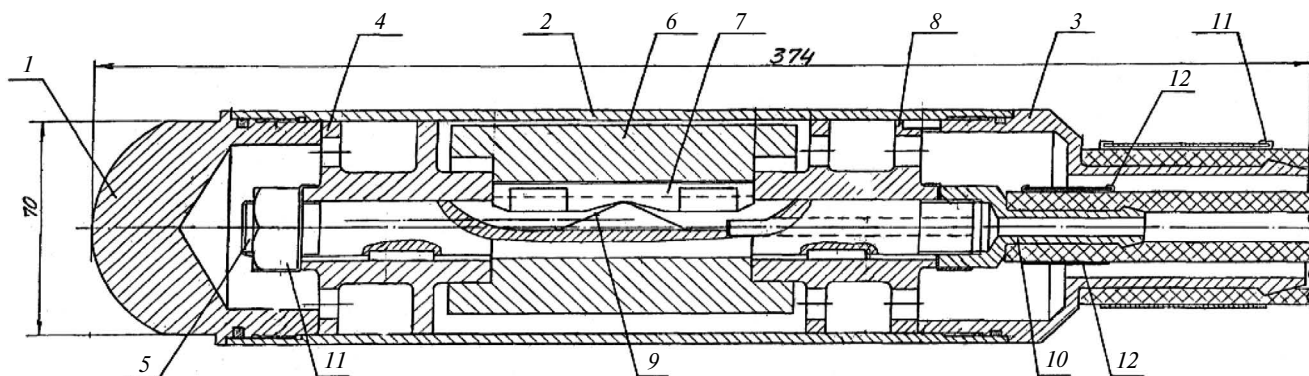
Глубинный пневматический вибратор: 1, 3 – оголовки; 2 – цилиндр; 4, 8 – крышки; 5 – ось; 6 – бегунок; 7 – лопатка; 9 – пружина; 10 – ниппель; 11 – гайка; 12 – шланг
